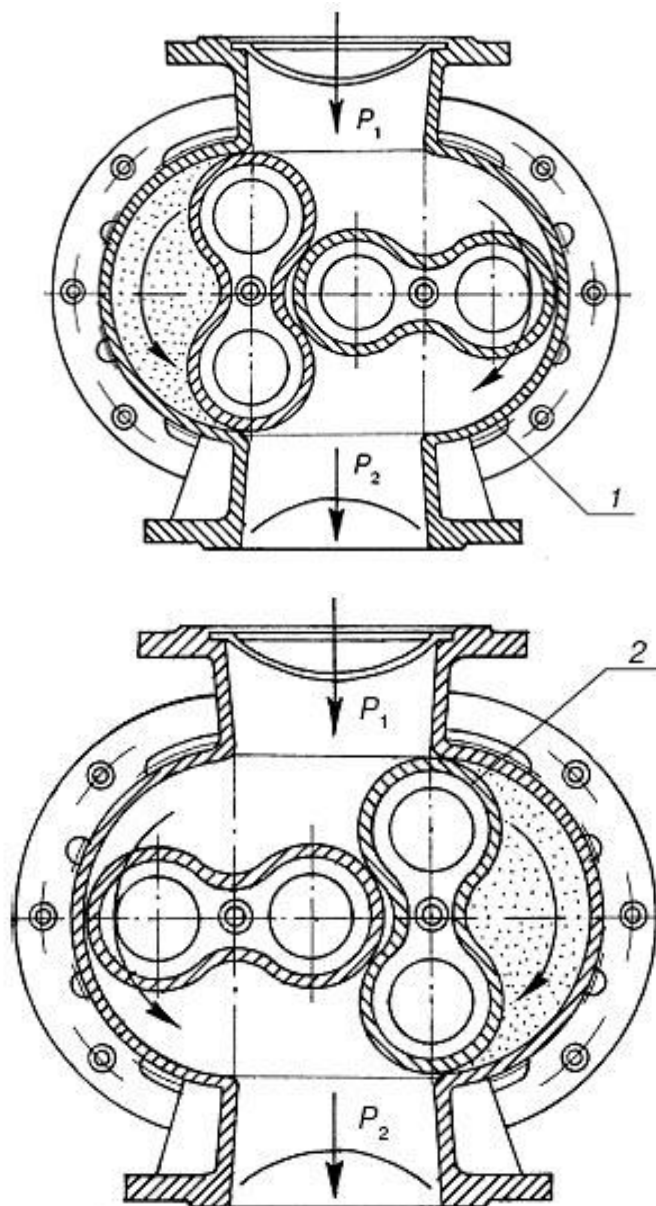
Схема ротаційного лічильника: 1-корпус; 2- ротор.
